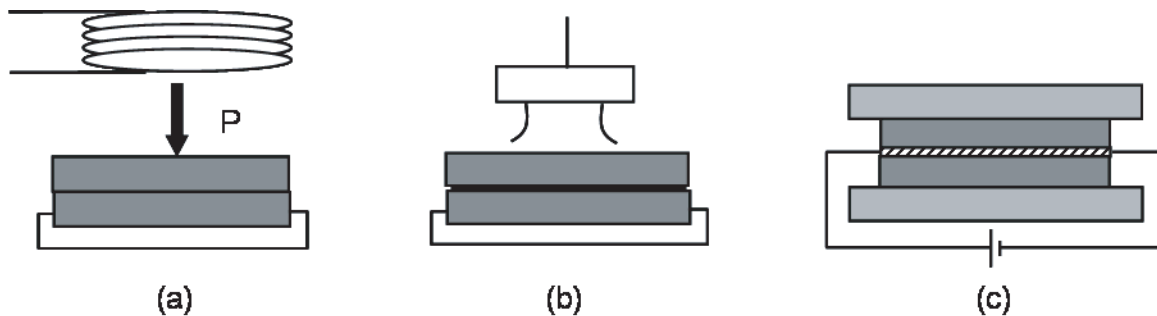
Représentation schématique : (a) du soudage par induction, (b) du soudage par micro-ondes, (c) du soudage par résistance
